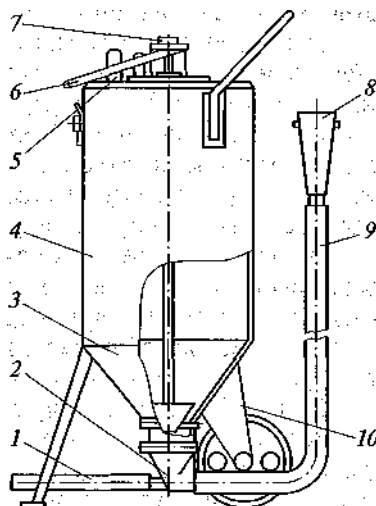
Пневмоагрегат конструкции ЦНИИОМТП:
